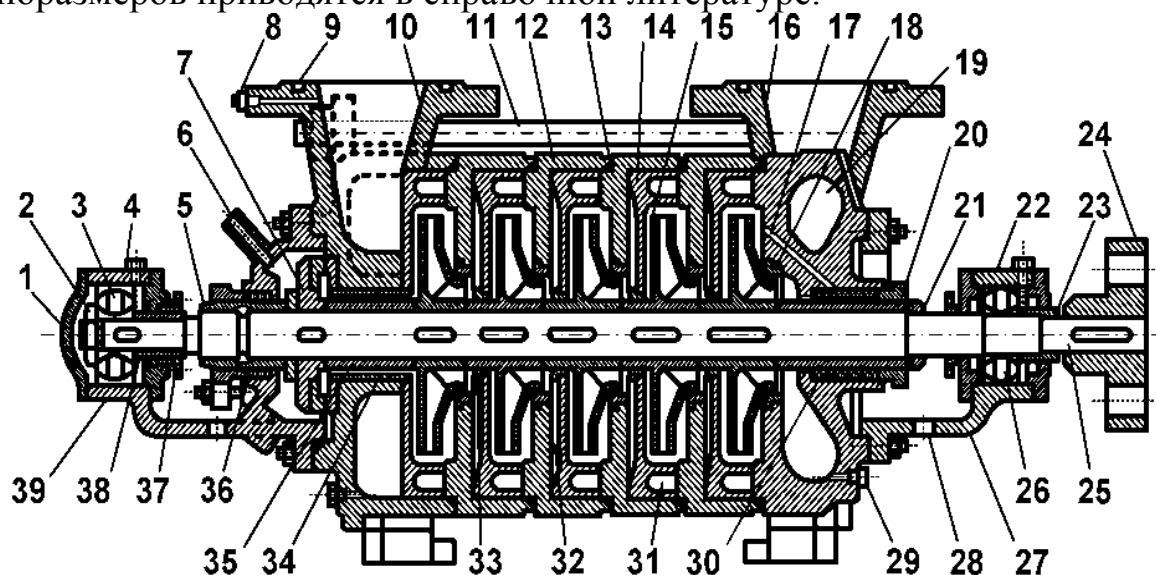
Конструкция насоса ЦНС300-300: 1 - глухая крышка; 2 и 21 - стопорная гайка; 3 и 26 - роликовые подшипники; 4 и 22 - задняя и передняя подшипниковая опоры; 5 и 20 - защитные втулки сальника; 6 - патрубок для дренажа воды из гидропаты; 7 - разгрузочный диск; 8 - гнездо для установки манометра; 9 - расточка под прокладку; 10 и 16 - напорный и всасывающий патрубки; 11 - стяжная шпилька; 12 - корпус промежуточной секции; 13 - резиновое кольцевое уплотнение; 14 - спиральный направляющий аппарат; 15 - рабочее колесо 2-й ступени; 17 - канал подвода воды на гидрозатвор сальника; 18 - уплотняющее кольцо рабочего колеса; 19 - кольцевой водораспределительный канал; 23, 35 и 38 - дистанционные втулки; 24 - полумуфта; 25 - вал; 27 и 39 - передний и задний фонари; 28 -
